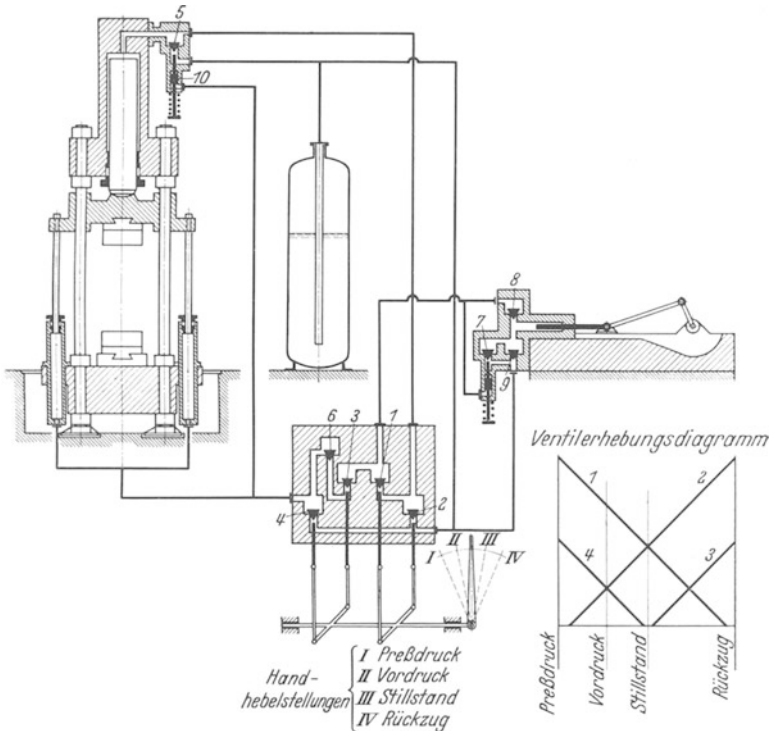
Steuerschema für eine Schmiedepresse mit direktem Pumpenbetrieb.
